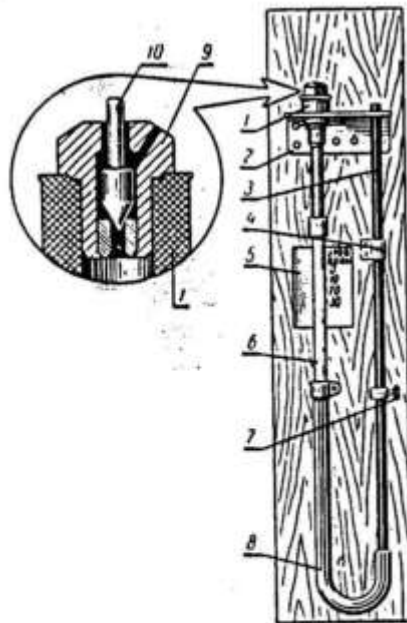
Прибор для проверки герметичности игольчатого клапана поплавковой камеры:
